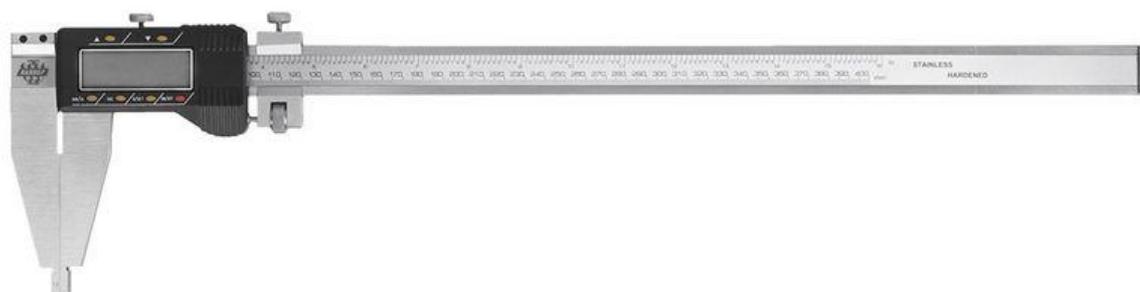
Общий вид штангенциркулей типа ШЦЦ-III
